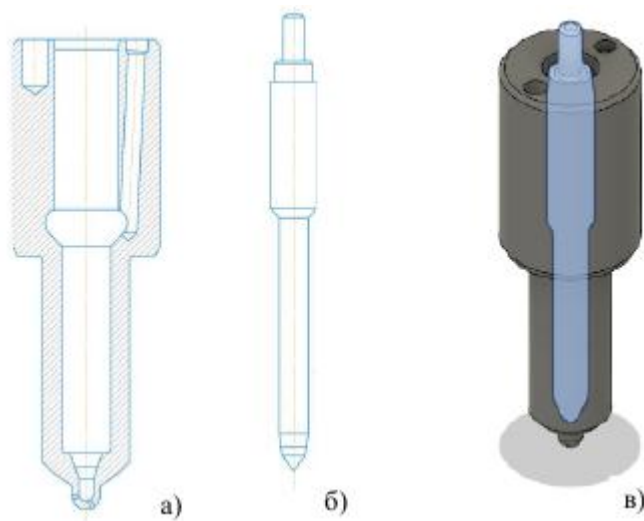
Принципова схема розпилювача форсунки: а - корпус, б - голка;
